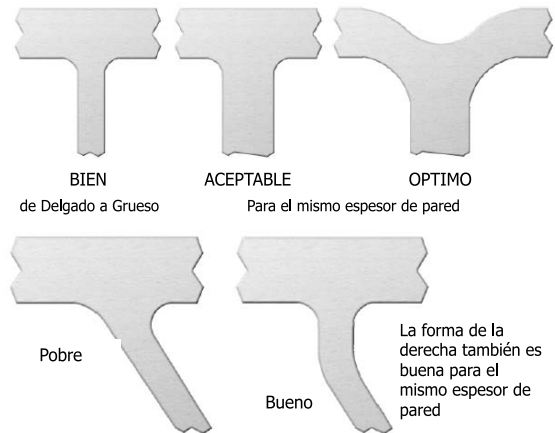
Formas recomendadas para unión de paredes Fuente: Hitchiner Manufacturing Co., Inc, Designing for investment casting, Technical Updated 2D1.
